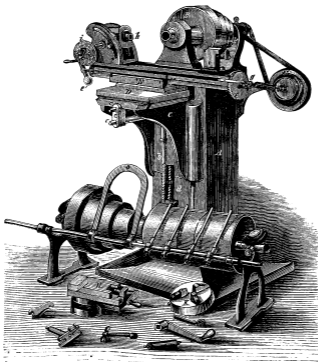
Amerikanische Werkzeug-Schneidemaschine.
